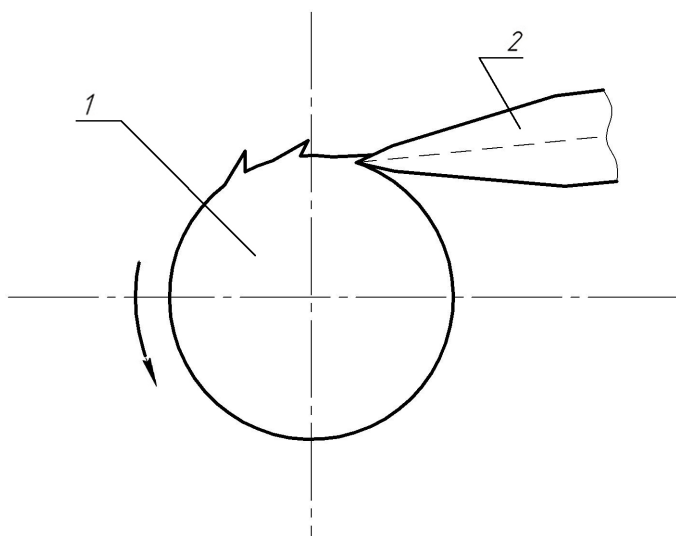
Подготовка поверхности детали под напыление методом насечки пневматическим зубилом: 1 – деталь; 2 – пневматическое зубило
